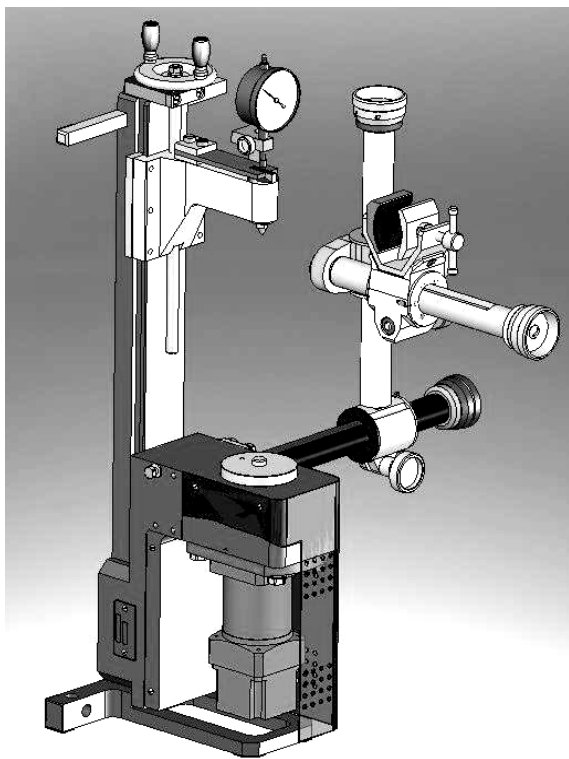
Сварка на поворотном приспособлении с вертикальной осью вращения
